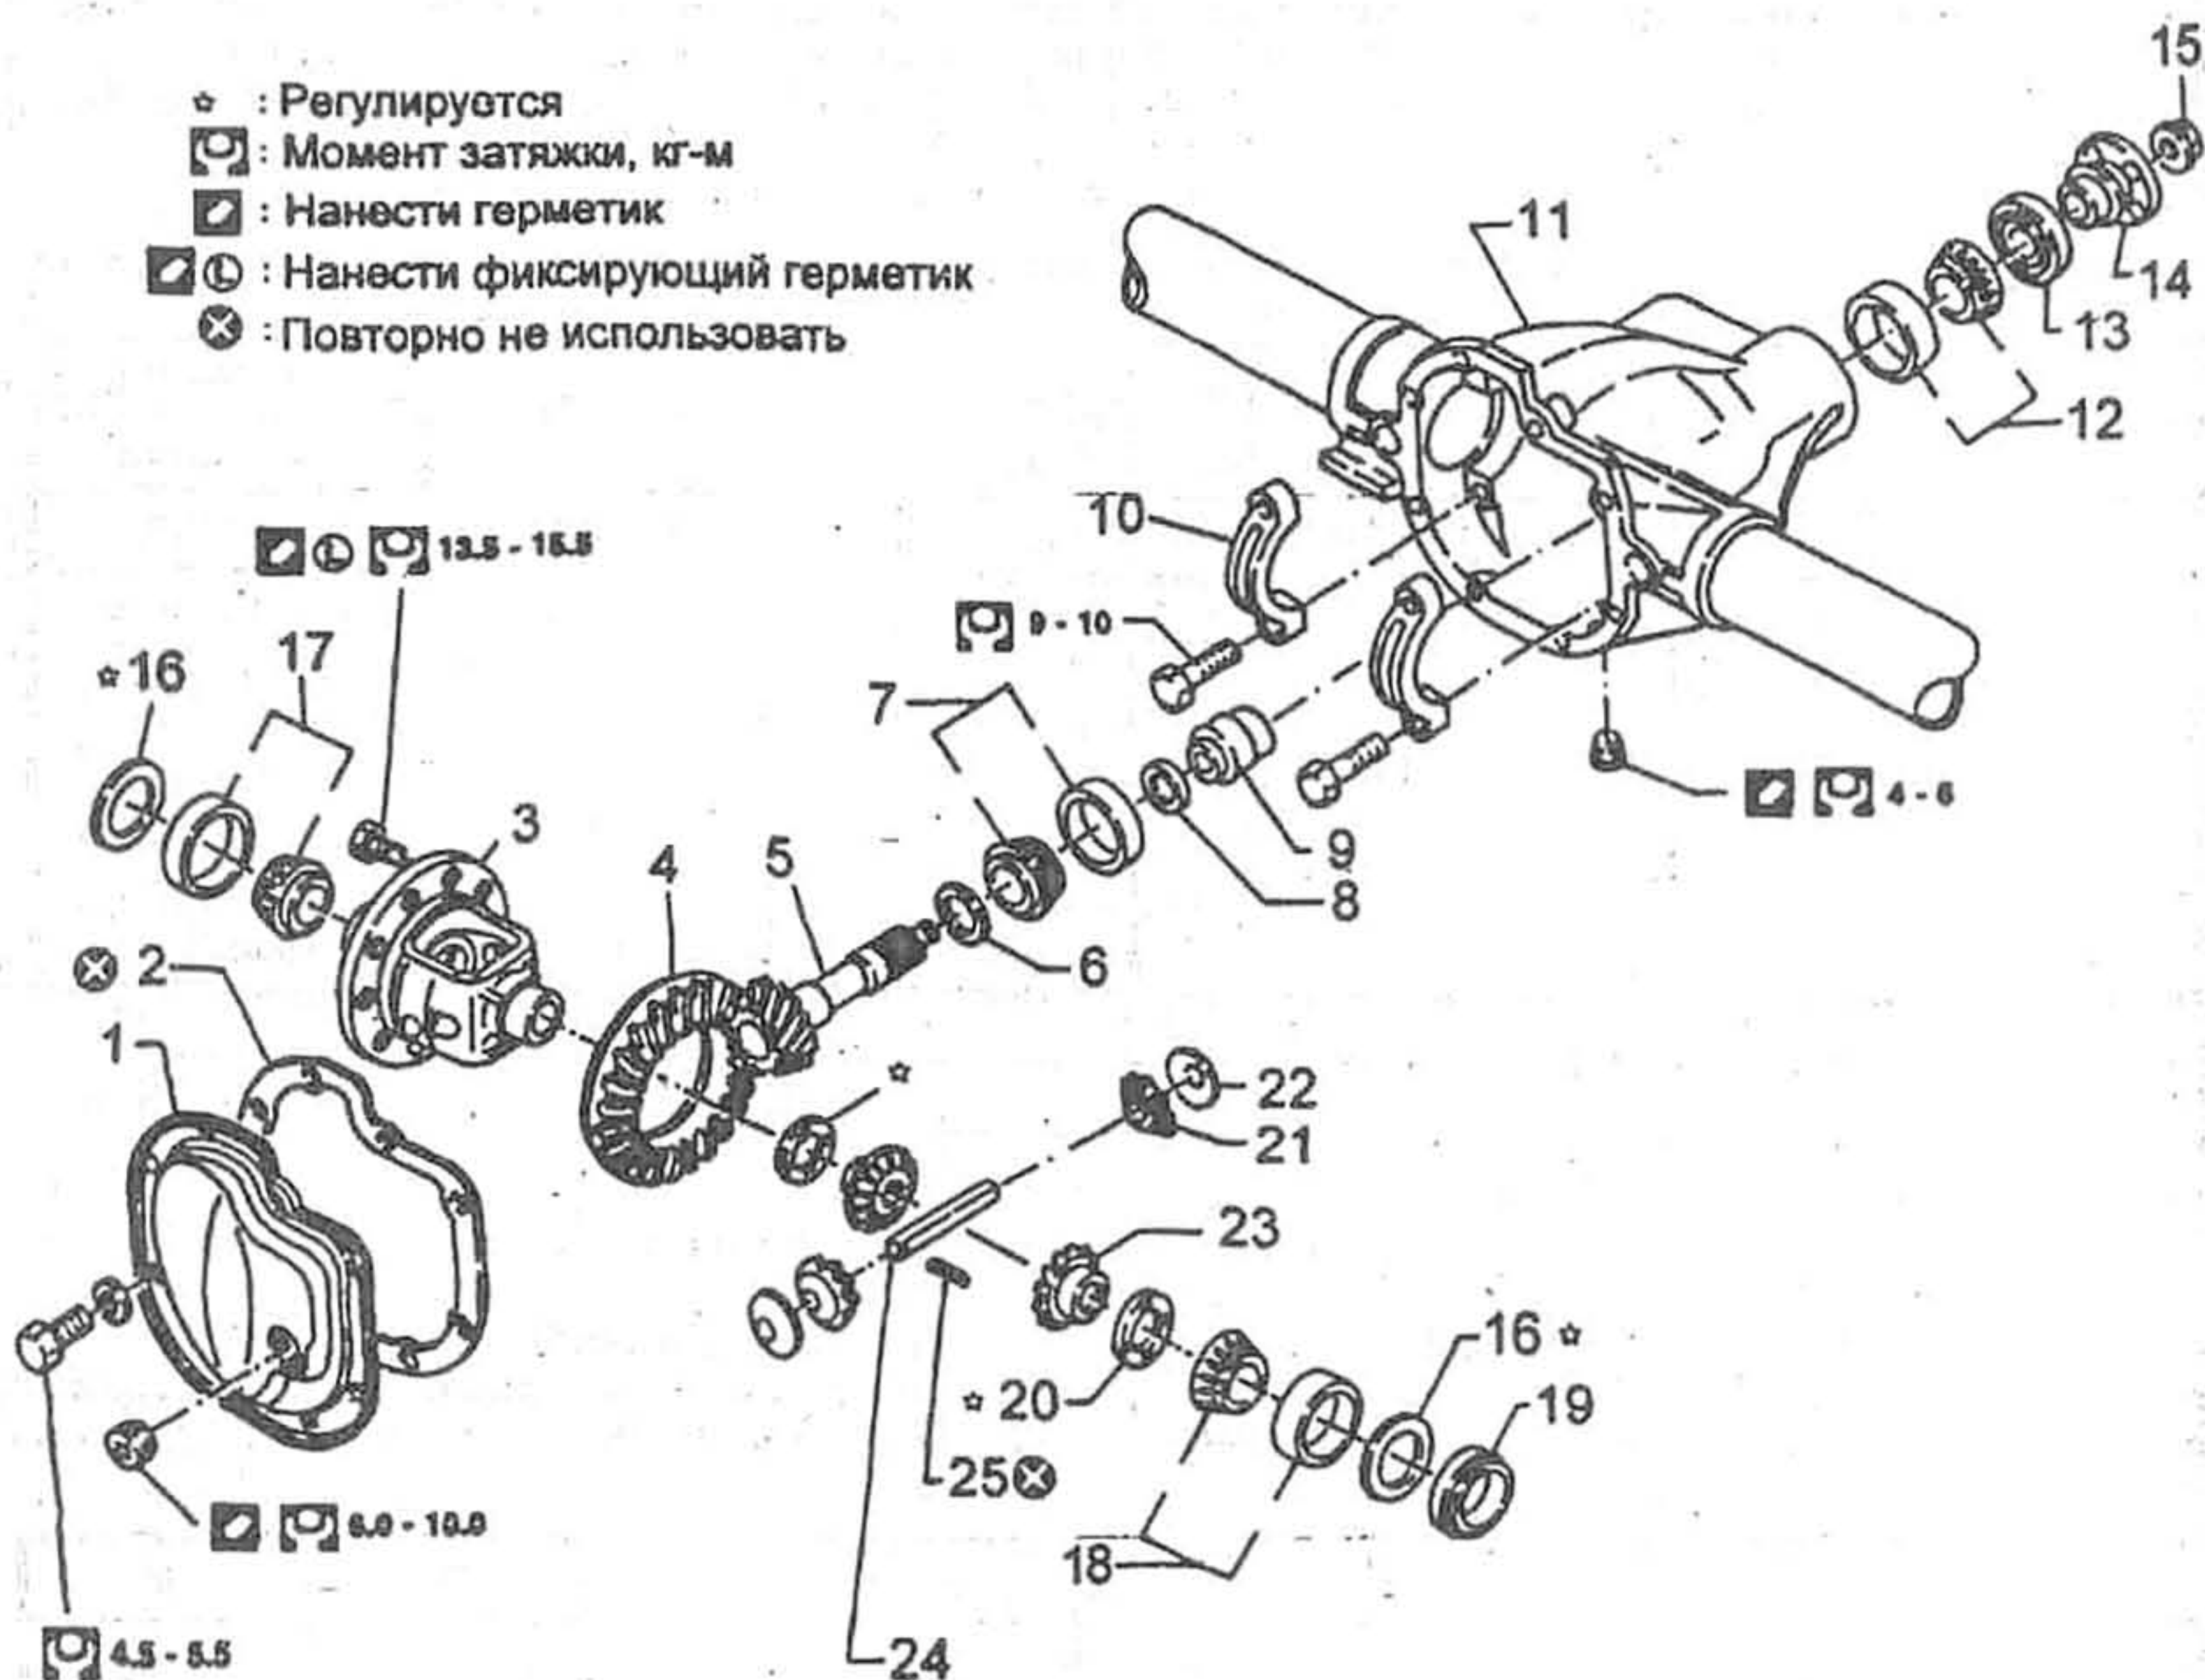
1. Задняя крышка. 2. Прокладка. 3. Дифференциал. 4. Ведомая шестерня. 5. Ведущая шестерня. 6. Регулировочная прокладка ведущей шестерни. 7. Задний подшипник ведущей шестерни. 8. Установочная шайба. 9. Втулка. 10. Крышки боковых подшипников. 11. Картер дифференциала. 12. Передний подшипник ведущей шестерни. 13. Сальник ведущей шестерни. 14. Соединительный фланец. 15. Гайка ведущей шестерни. 16. Регулировочная прокладка бокового подшипника. 17. Левый подшипник. 18. Правый подшипник. 19. Втулка бокового подшипника. 20. Упорная шайба бокового подшипника. 21. Сателлит. 22. Упорная шайба сателлита. 23. Боковая шестерня. 24. Ось сателлитов. 25. Штифт.
